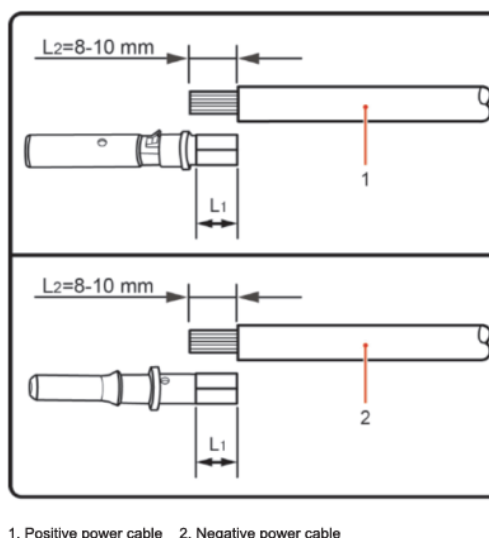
Conexión de los cables de potencia CC en entrada (1)
